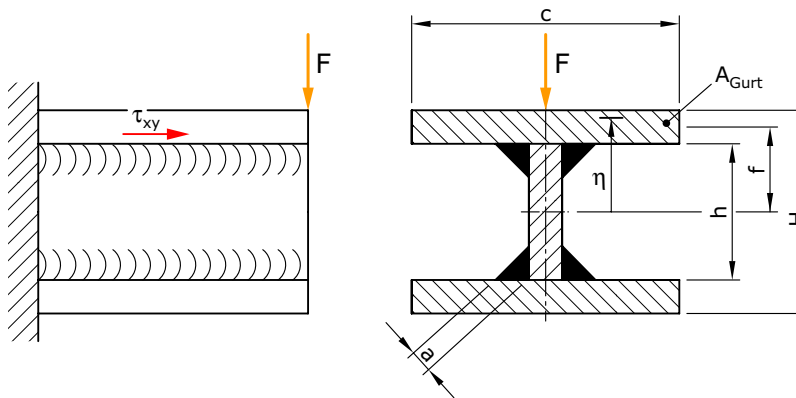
WS) Mit Halsnähten geschweisster Biegeträger
